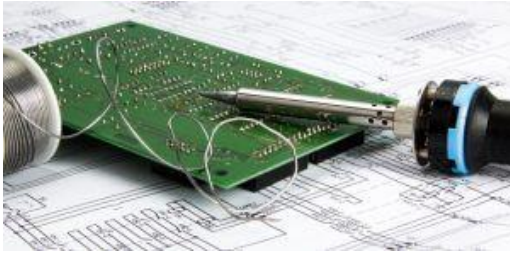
Soudage au fer dans l'électronique
